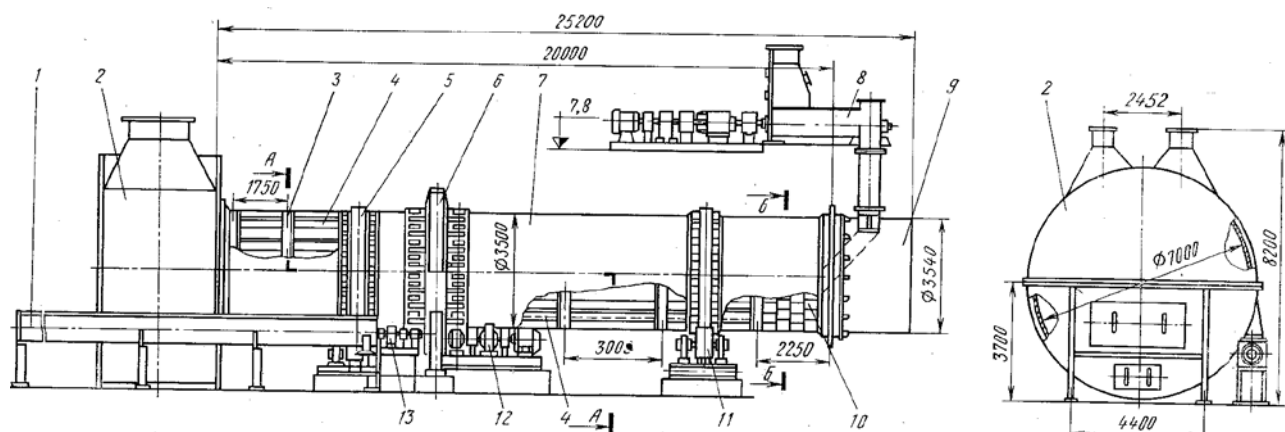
Барабанна сушарка ПСА-2 - 1-шнек для сухого жому; 2-корпус нерухомий; 3,4,10-насадки; 5-бандаж опорний; 6 шестерня вінцева; 7-корпус; 8-шнек-змішувач; 9-царга нерухома; 11- опорний ролик; 12-привід апарата; 13-привід шнека для сухого жому.
